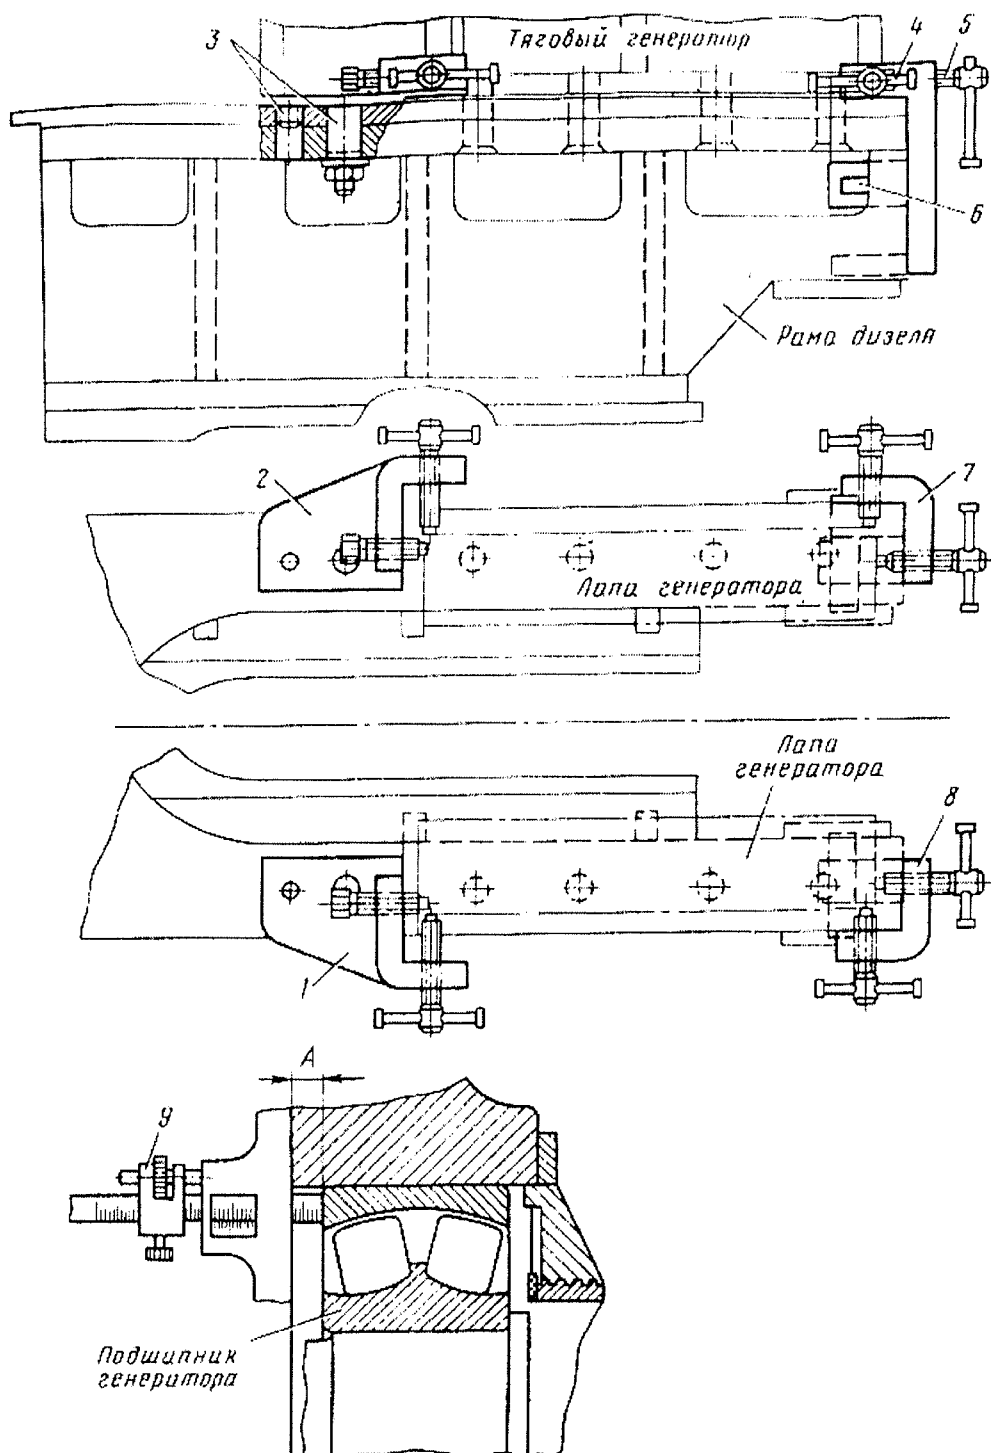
Приспособление для регулировки положения тягового генератора на раме дизеля
